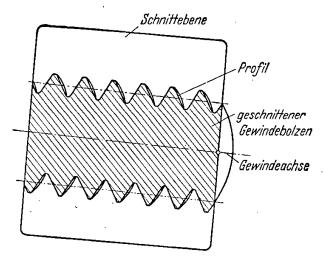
Achsenschnitt durch einen Gewindebolzen.
